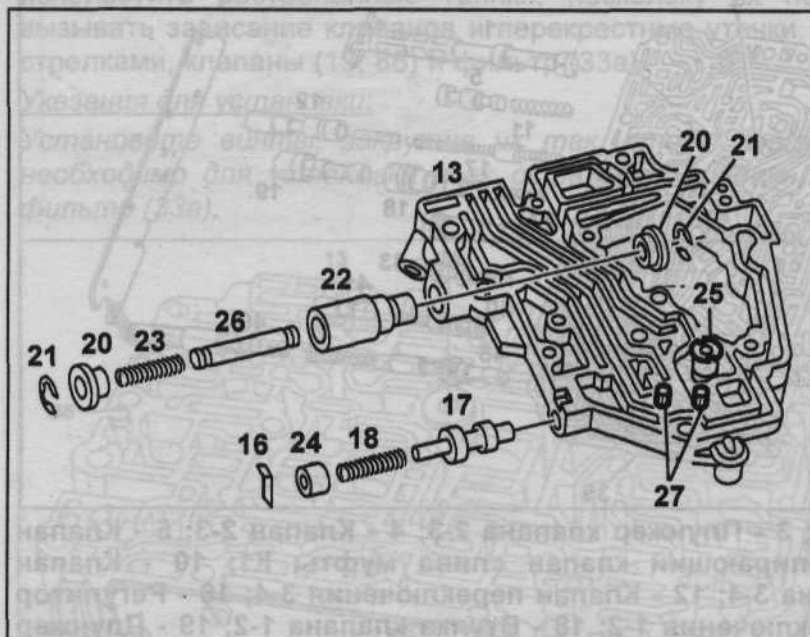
13 - Нижняя часть клапанной коробки; 16 - Стопорная пластина; 17 - Клапан вспомогательного насоса; 18 - Пружина; 20 - Втулка; 21 - Стопорное кольцо; 22 - Блокирующий клапан; 23 - Пружина; 24 - Заглушка; 25 - Клапан; 26 - Шток; 27 - Фильтры.
